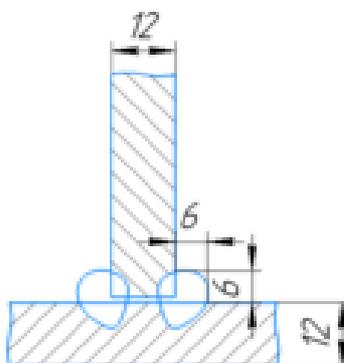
Общий вид сварного шва №3.
